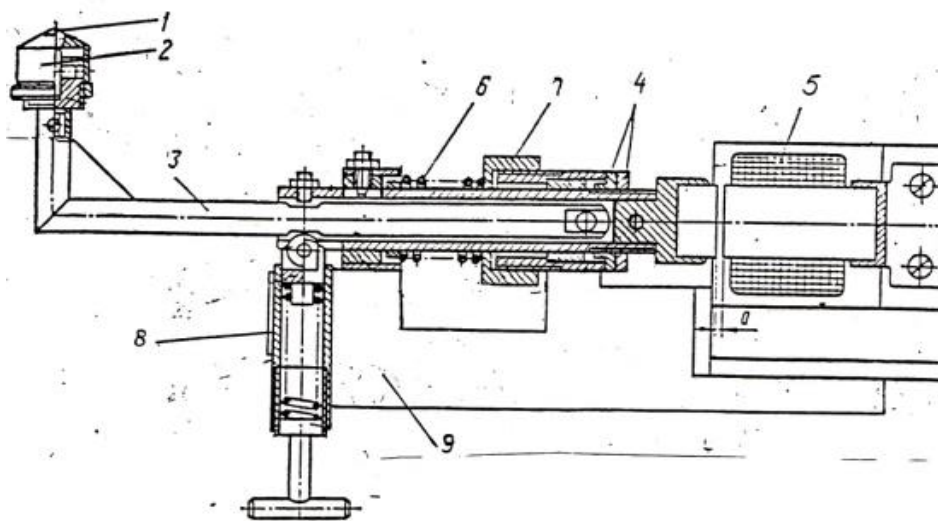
Схема обробки зовнішньої циліндричної поверхні обкатуванням
